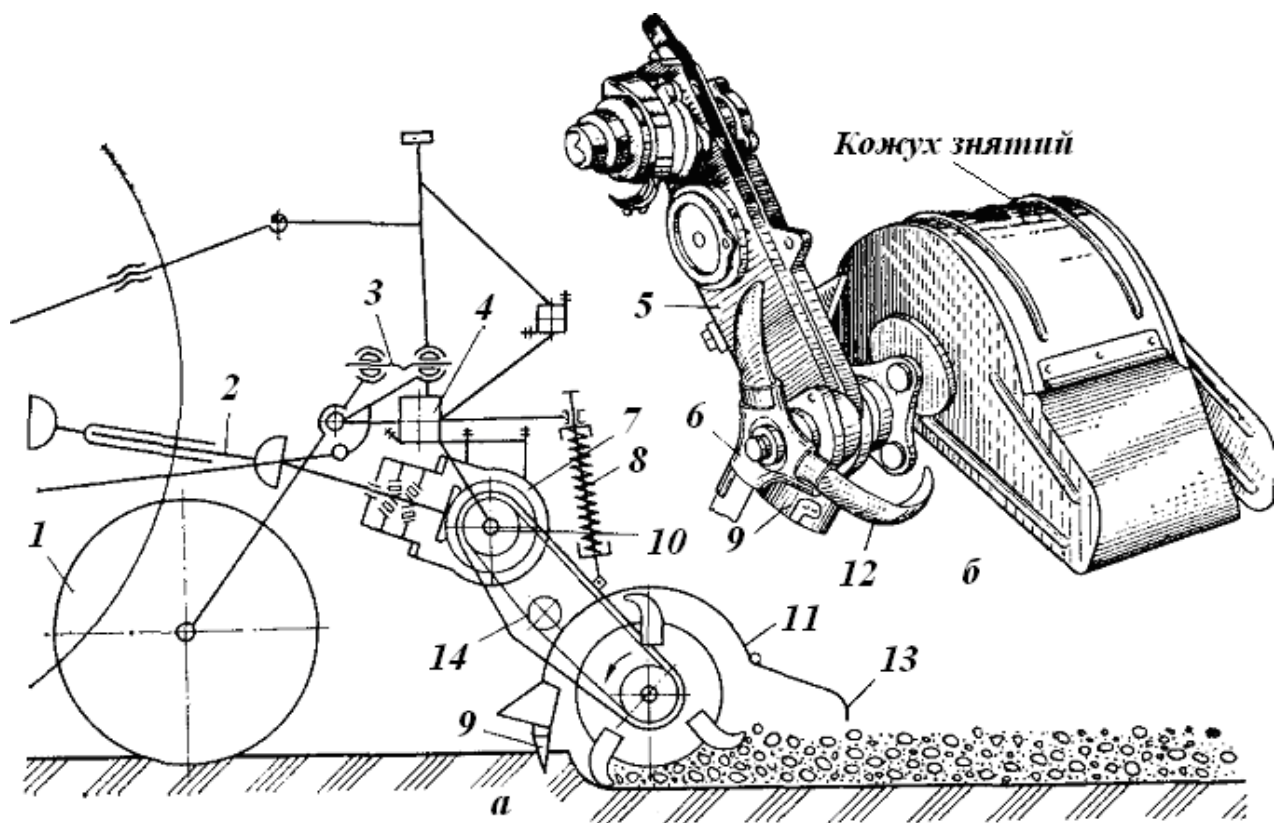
Фрезерний культиватор КФ-5,4: а - принципова схема; б - робоча секція;
